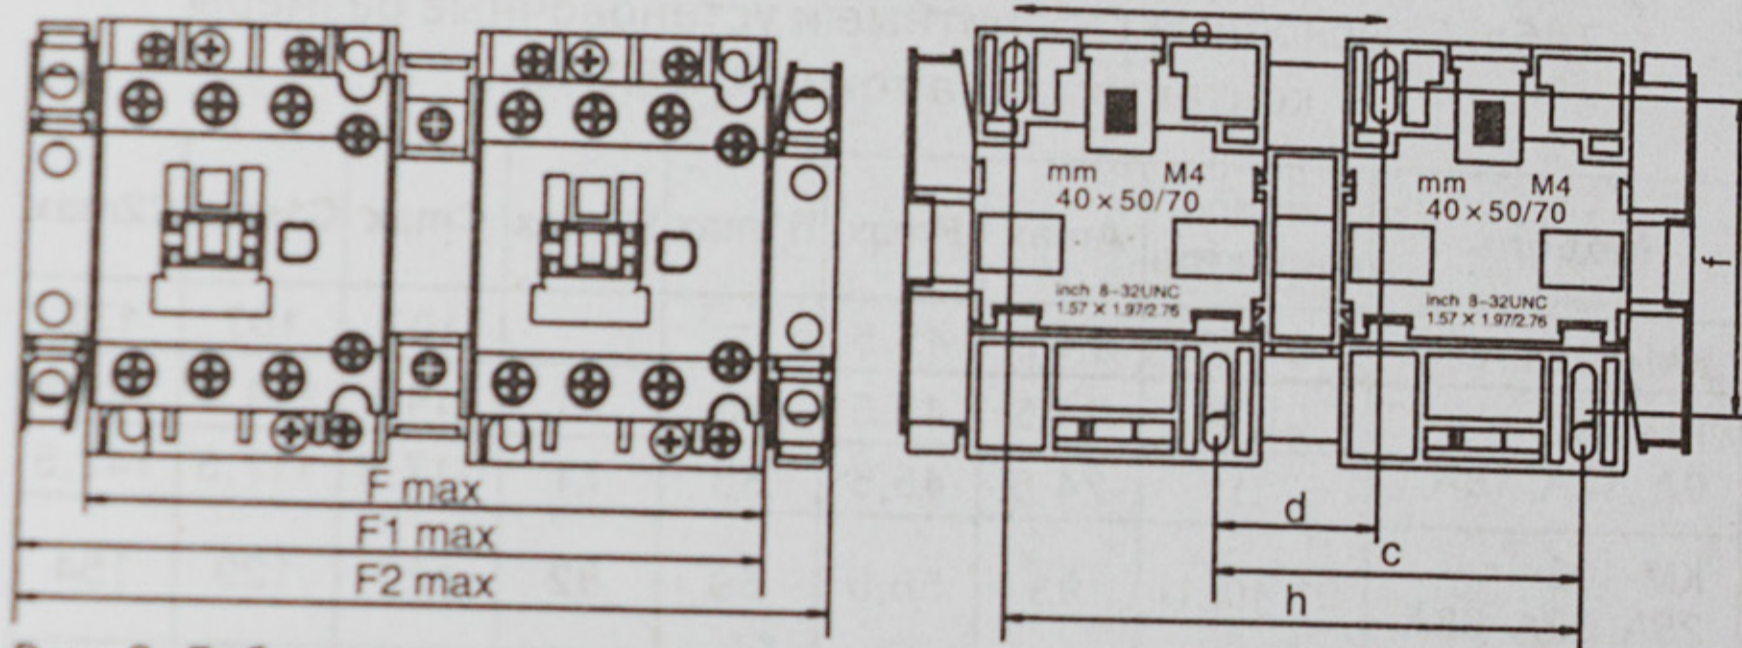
Габаритные и установочные размеры контакторов с реверсивной сборкой на токи 9А–38А, мм.
